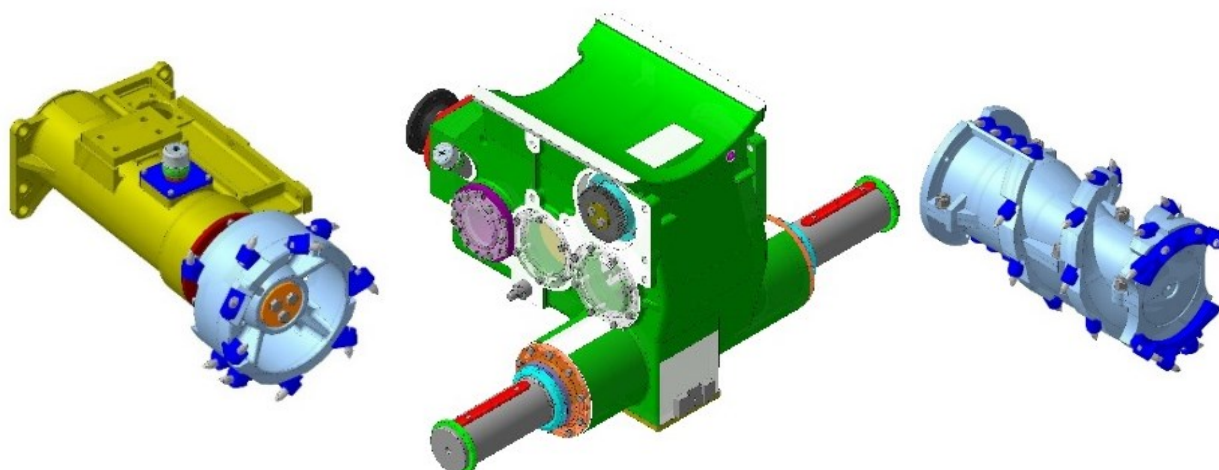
Редуктор бермовых фрез и отрезных барабанов
